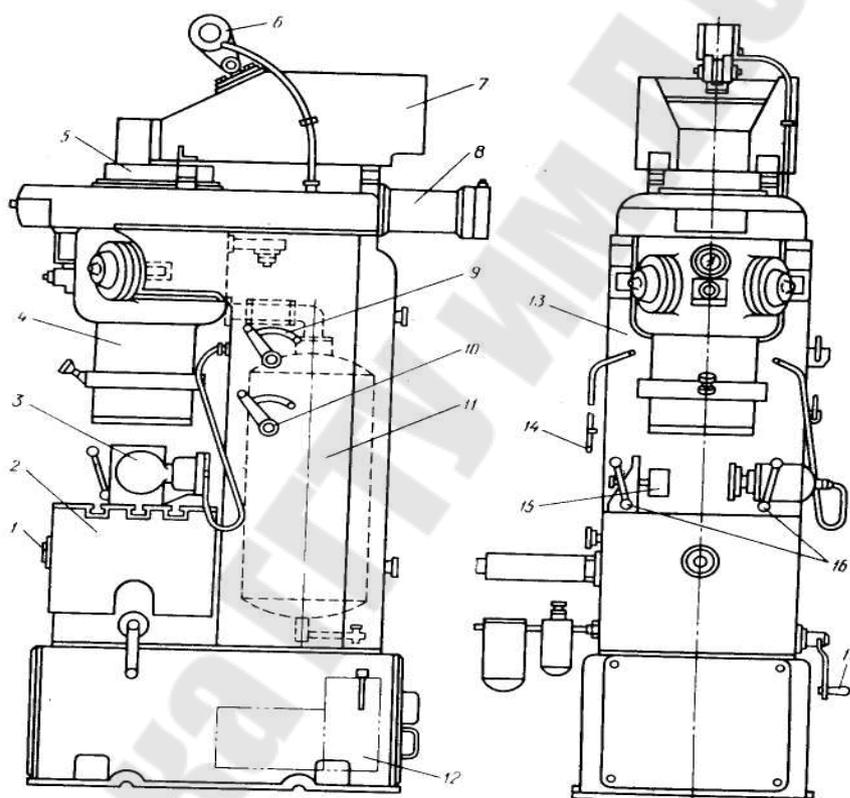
Общий вид пескодувной машины мод. 306
